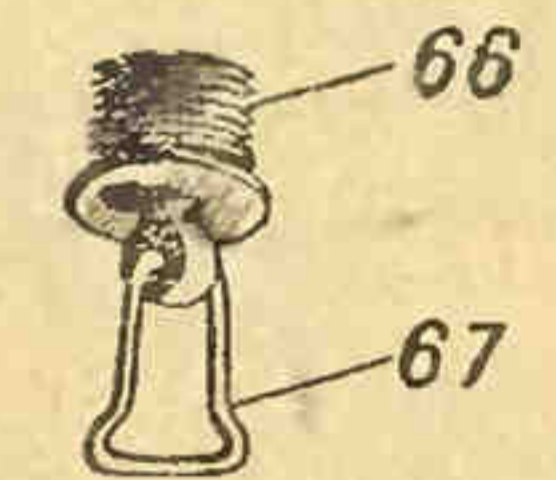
Завертка: 66 — завертка; 67 — кольцо.
